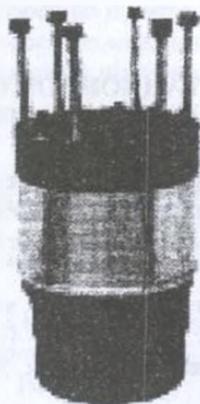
Вид судового цилиндра 6Д49.36 в сборе
